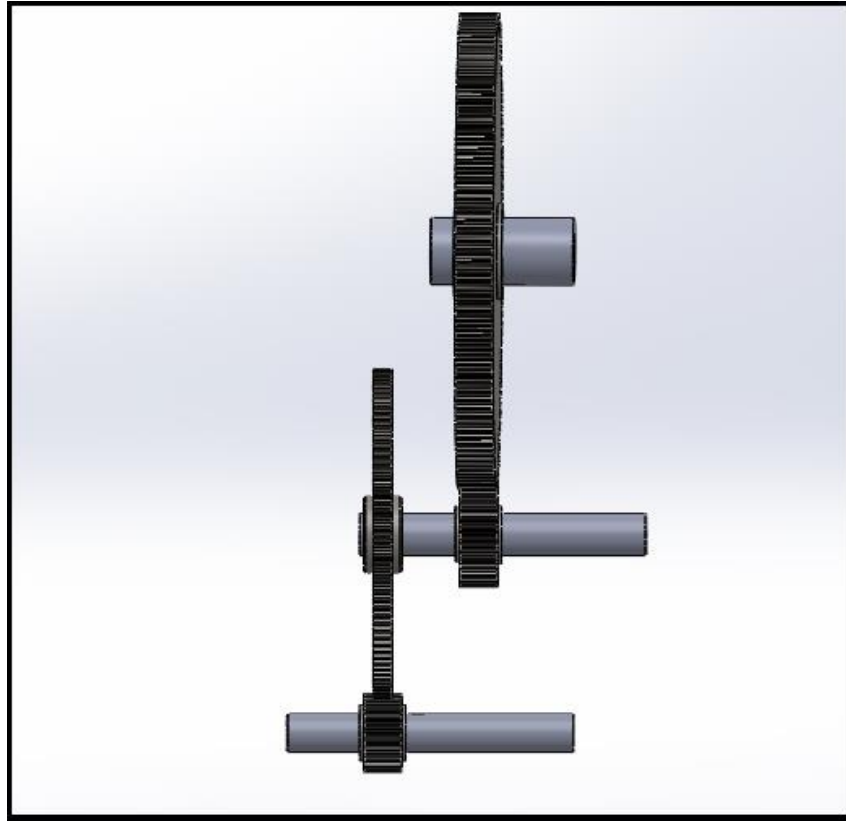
Montagem dos elementos internos do redutor, vista frontal.(Autor, 2022)
